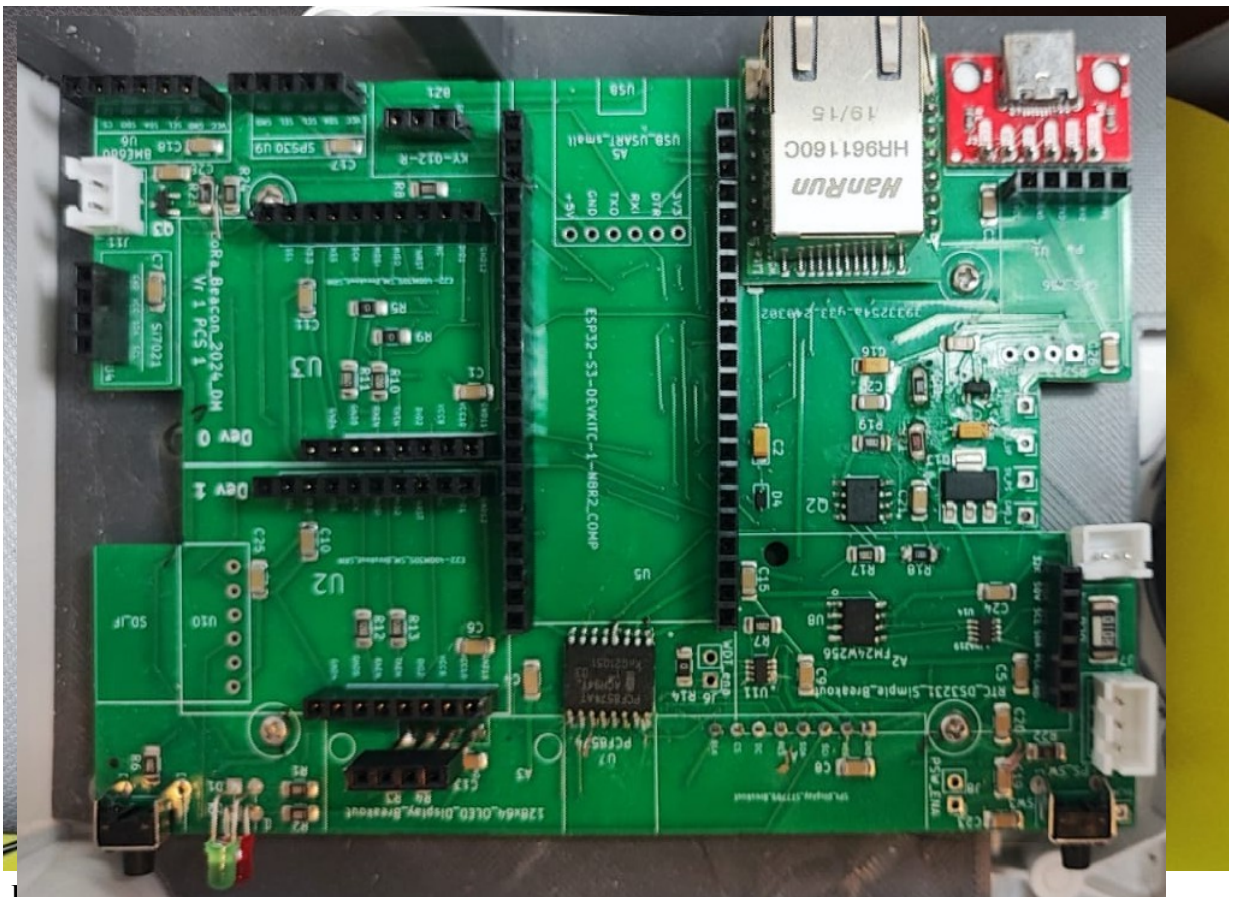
PCB Maxi a montaggio ultimato senza moduli ad innesto.
